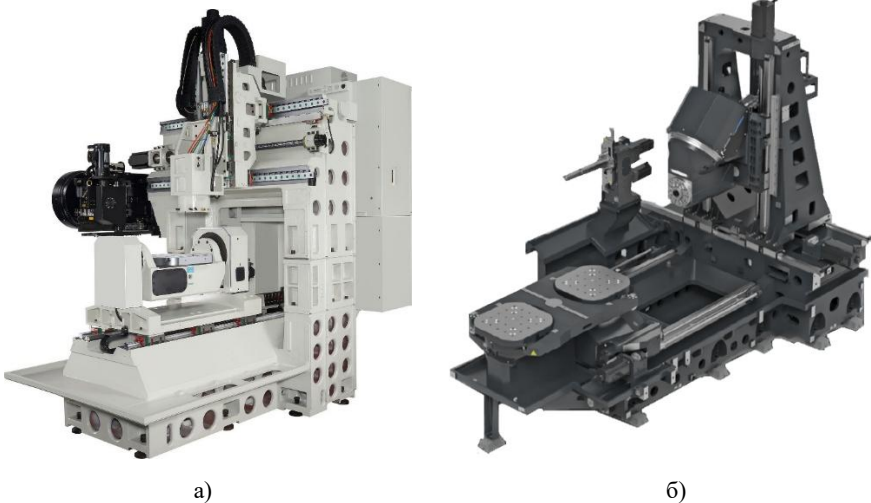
5-осьові фрезерні верстати з ЧПК: а – U 600 компанії Takumi; б – серії F компанії HELLER
